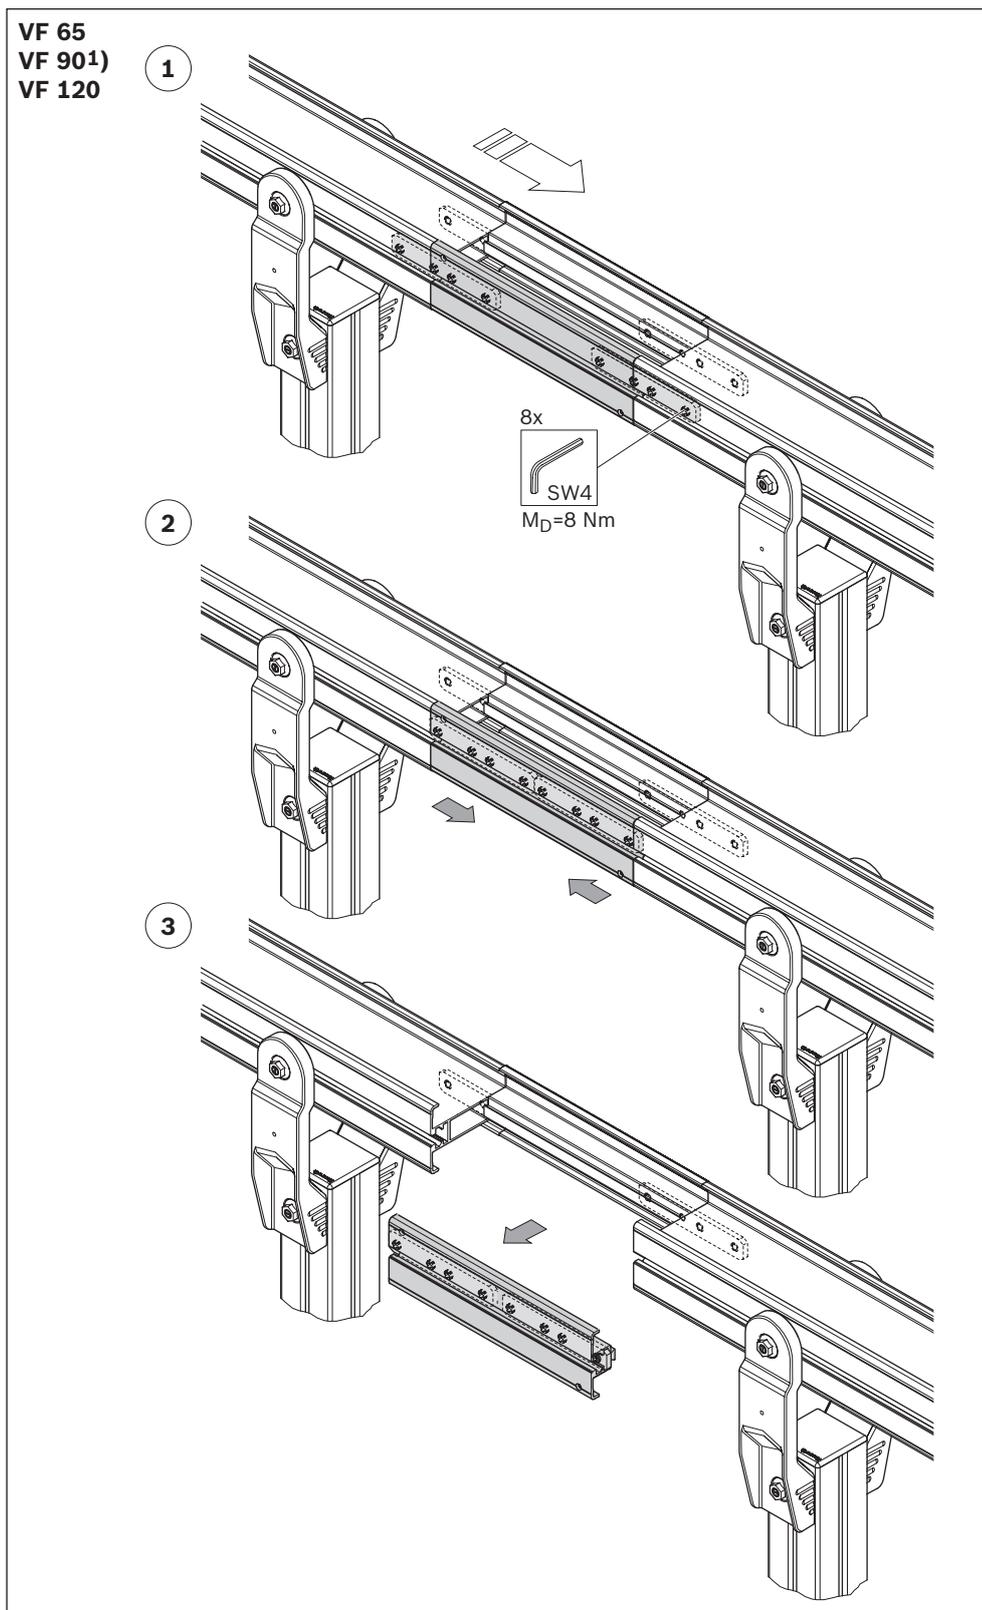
Sistema AL, apertura/cierre del módulo de montaje
